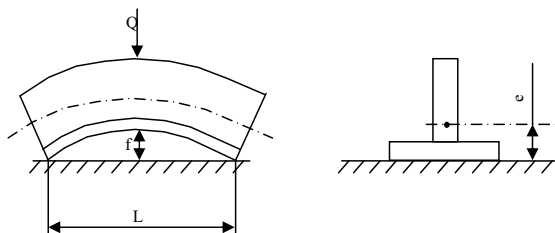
Расчетная схема при сварке балки таврового сечения
